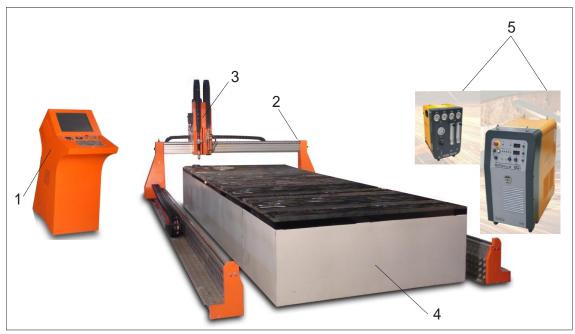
Установка плазменного раскроя металла (плазморезка)
